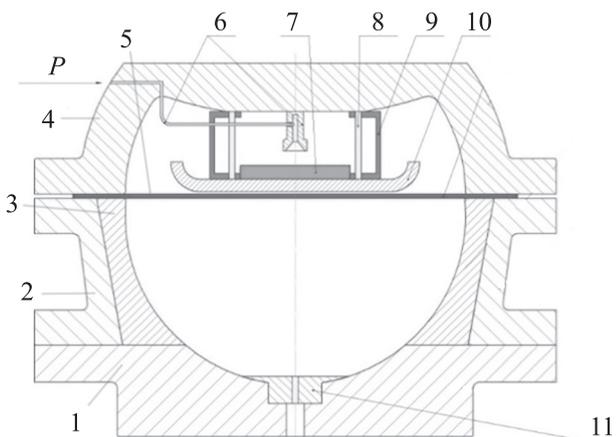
Общий вид штамповки «полусфера» [2], изготовленной методом газовой формовки в режиме сверхпластичности материала из титанового сплава VT-23
